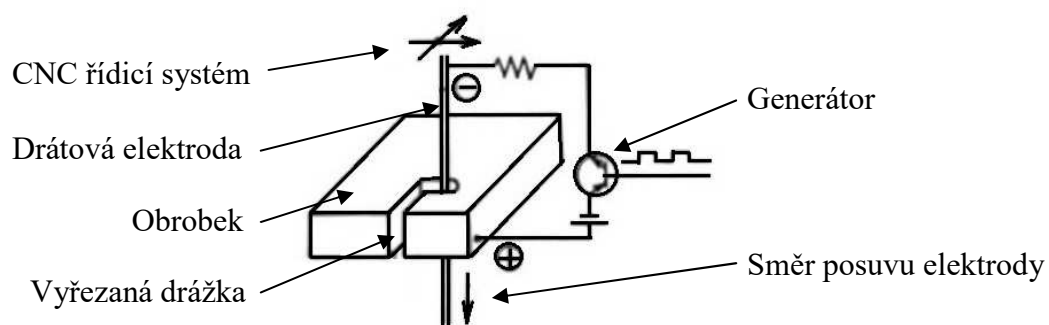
Princip zařízení pro elektroerozivní obrábění [21]
